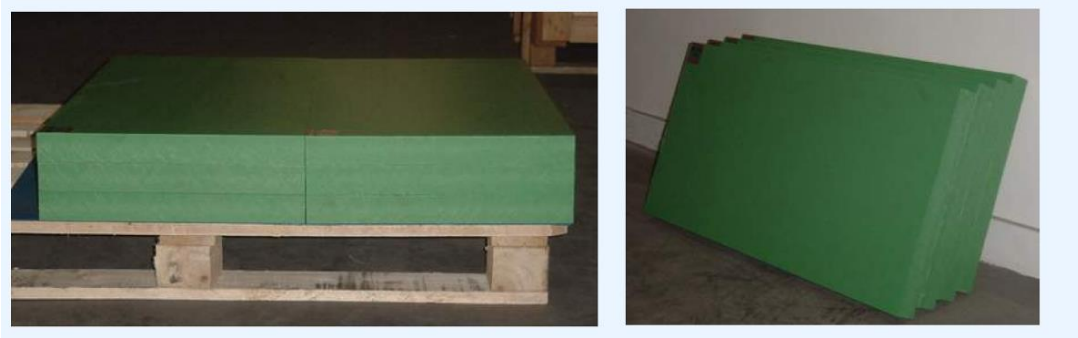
Almacenamiento correcto (horizontal) e inadecuado (vertical) de las planchas de cortado
